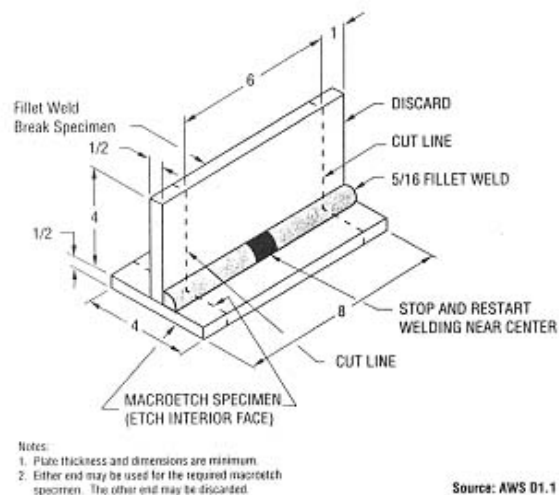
Plancha de ensayo para calificación de soldador AWS para soldaduras de filetes (Opción 1).
